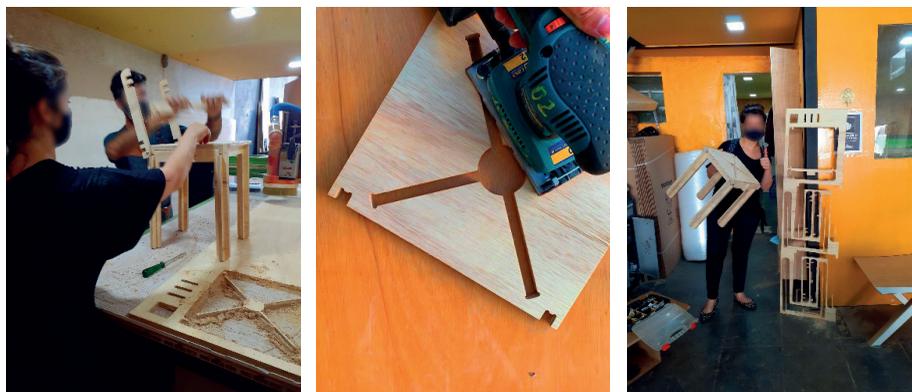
Fabricação, retirada das peças e montagem do mobiliário
